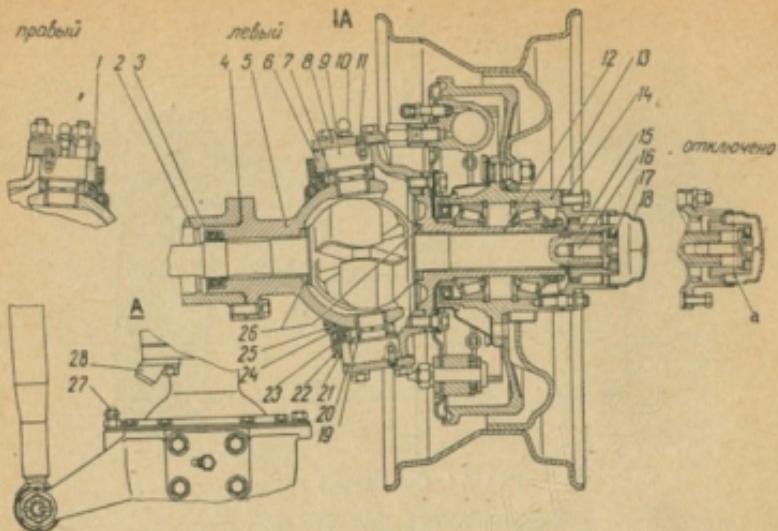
Поворотный кулак автомобиля УАЗ-469Б:
